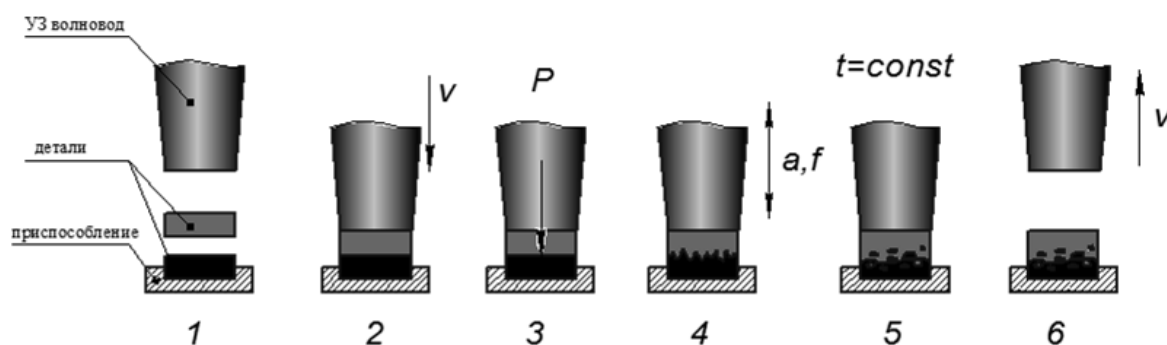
Цикл ультразвуковой сварки
